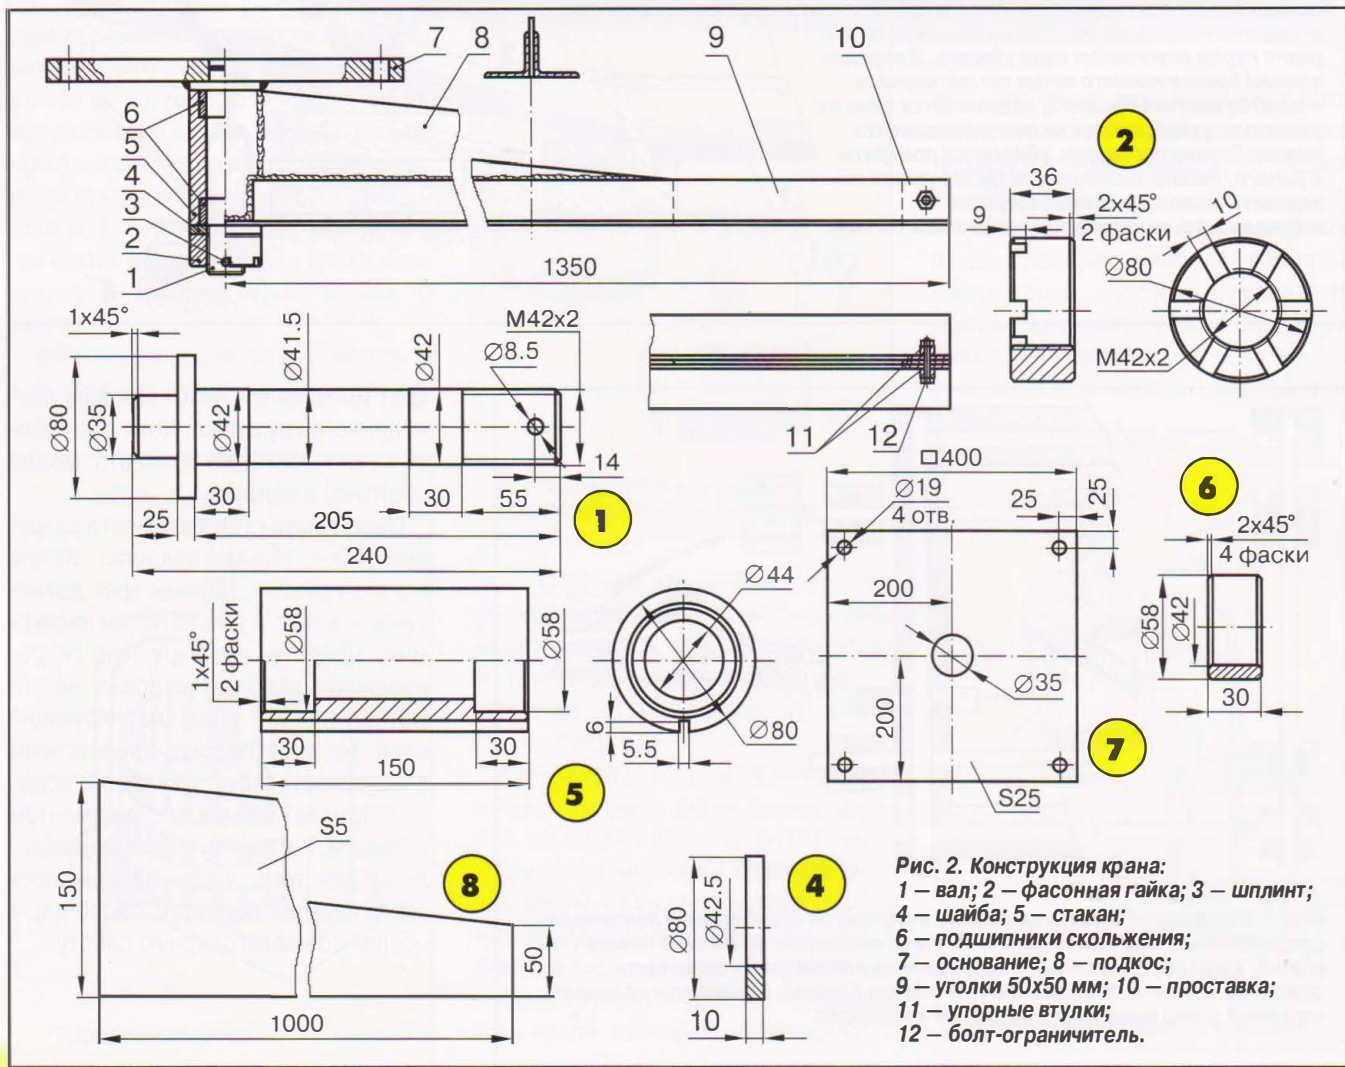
Конструкция крана: 1 — вал; 2 — фасонная гайка; 3 — шплинт; 4 — шайба; 5 — стакан; 6 — подшипники скольжения; 7 — основание; 8 — подкос; 9 — уголки 50х50 мм; 10 — проставка; 11 — упорные втулки; 12 — болт-ограничитель.
